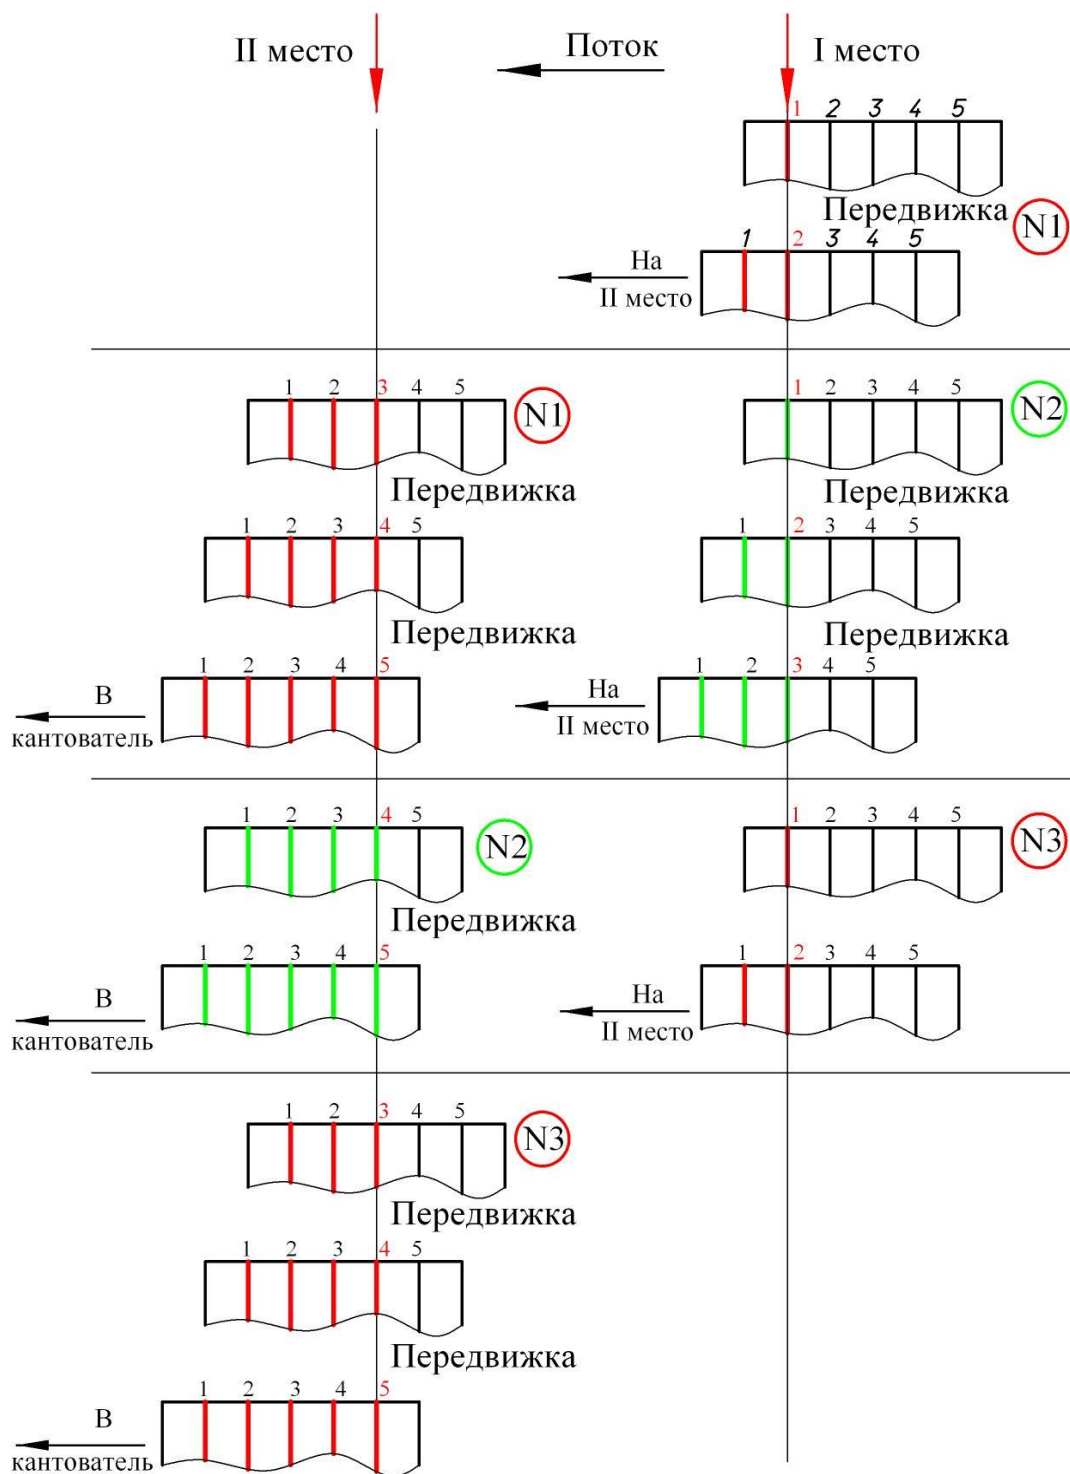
Схема сварки на двухместном стенде пяти стыковых листовых полотнищ:
